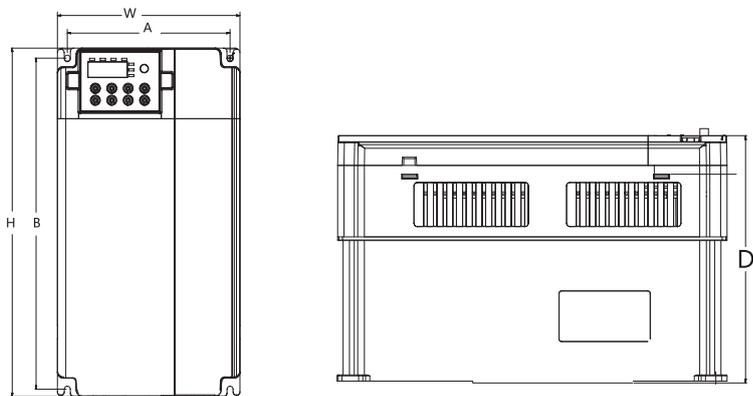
FU9000D系列 塑胶结构外型尺寸及安装尺寸示意图
